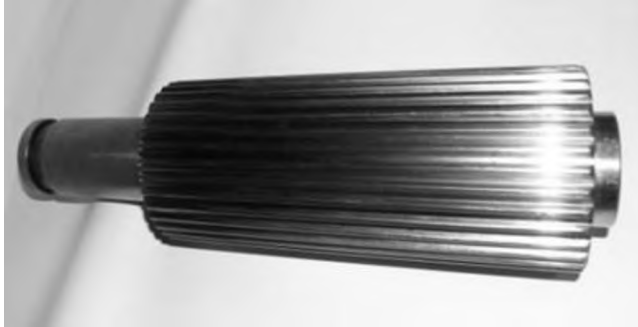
Зовнішній вигляд шліцьової оправки
